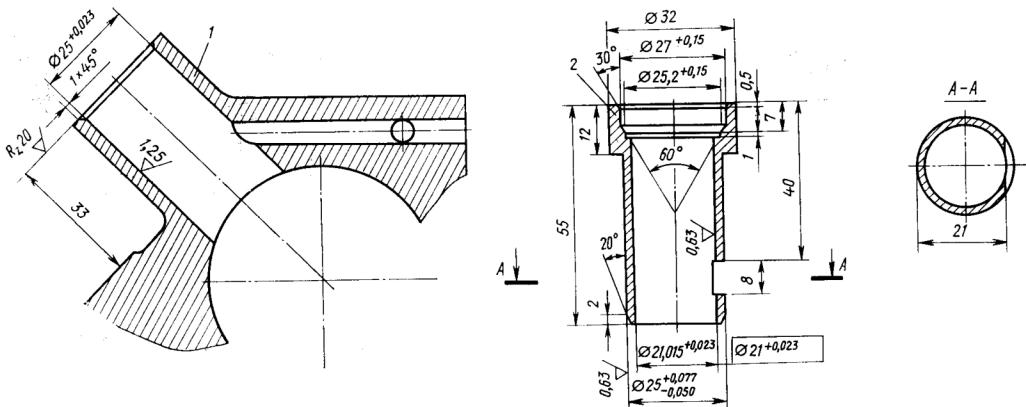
Расточка картера двигателя под ремонтные втулки бонок толкателя:
